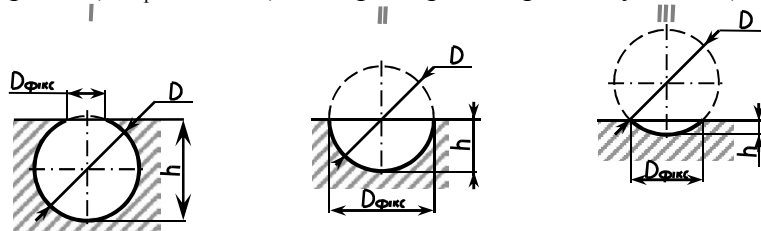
Схеми трьох варіантів розташування поверхневої пори в зварному шві.
